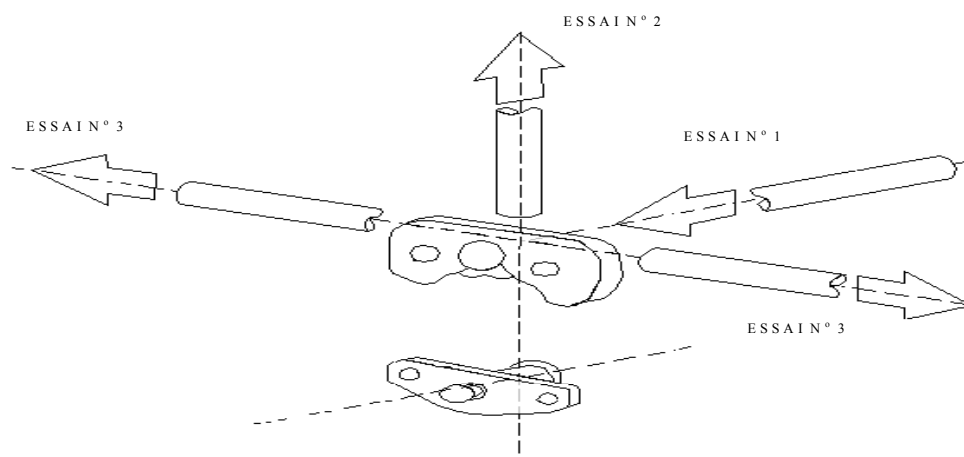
Directions d'application des forces sur la serrure de porte lors des essais statiques».
